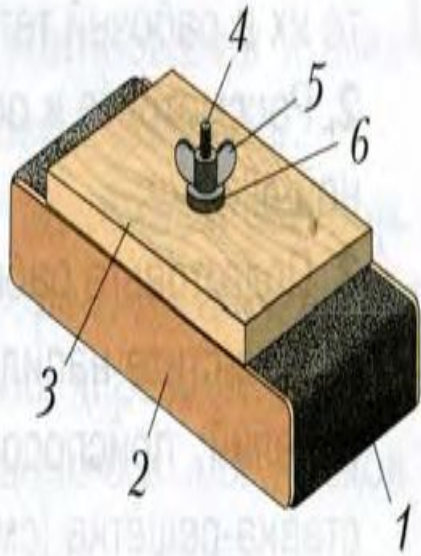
Зачистка больших поверхностей шлифовальной шкуркой: 1 – обрабатываемая поверхность; 2 – деревянный брусок; 3 – шлифовальная шкурка
